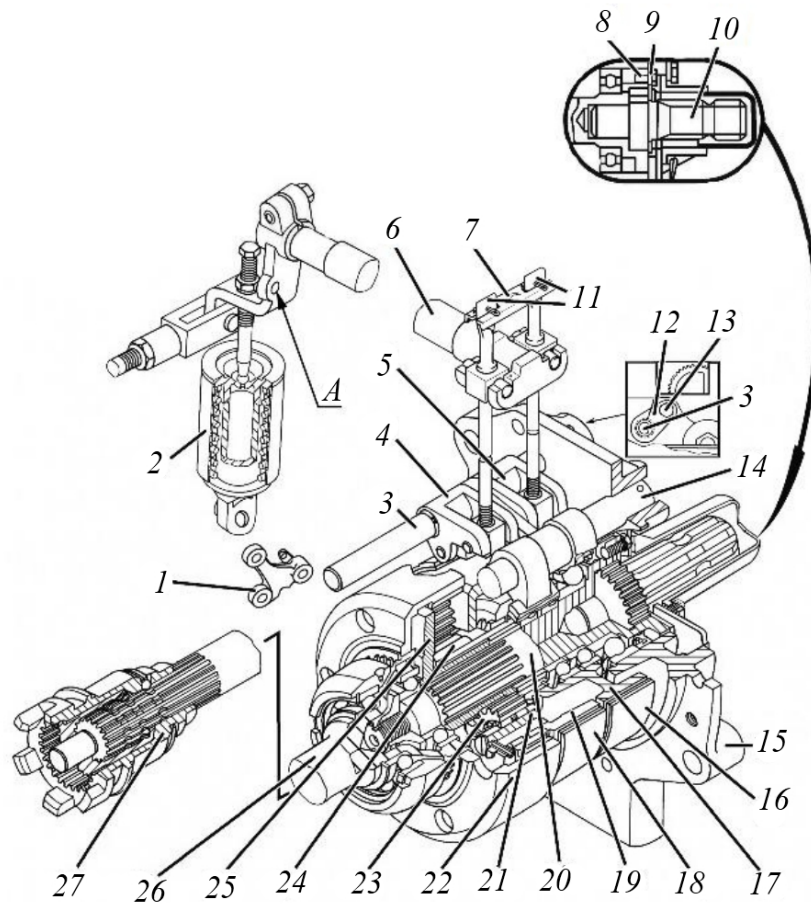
Планетарный редуктор заднего вала отбора мощности «Беларус-82.1»:
